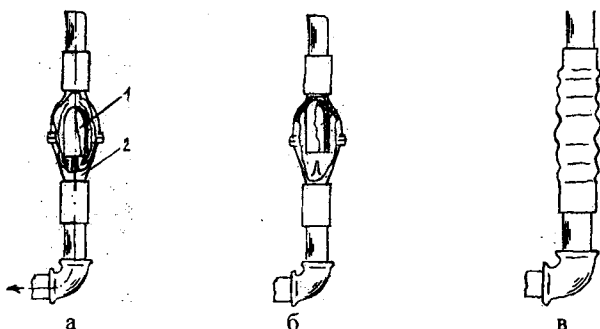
Схемы монтажа и положений клапана предохранителя:
